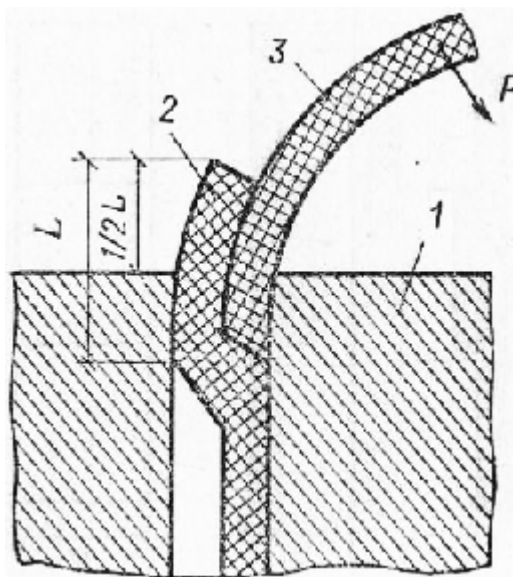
Испытание образцов на отдир 1 — зажимное устройство; 2 — деталь раструба или муфты; 3 — деталь трубы
